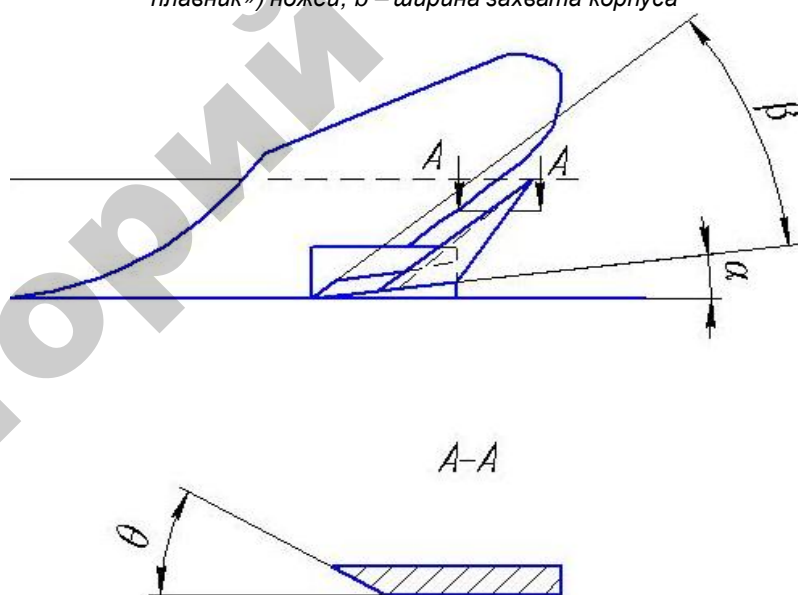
Корпус плуга с горизонтальным и вертикальным (типа «акулий плавник») ножами
